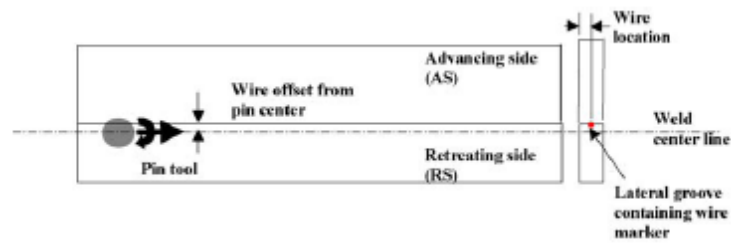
Configuração das chapas de metal antes da soldadura. Antes da soldadura um fio contínuo foi colocado, num sulco, entre as chapas.
